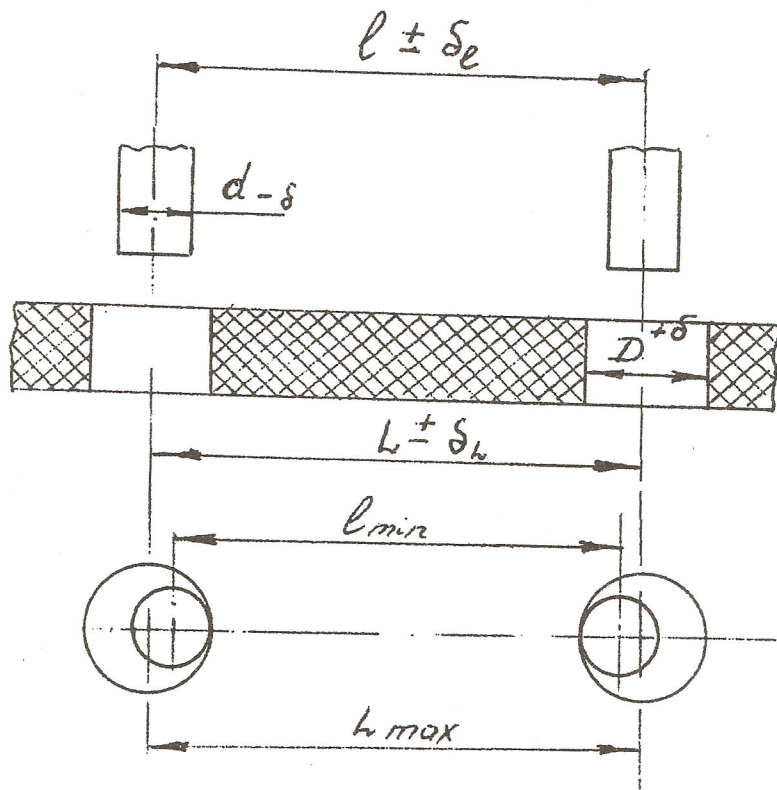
Схема сборки деталей, сопрягаемых по двум цилиндрическим поверхностям
